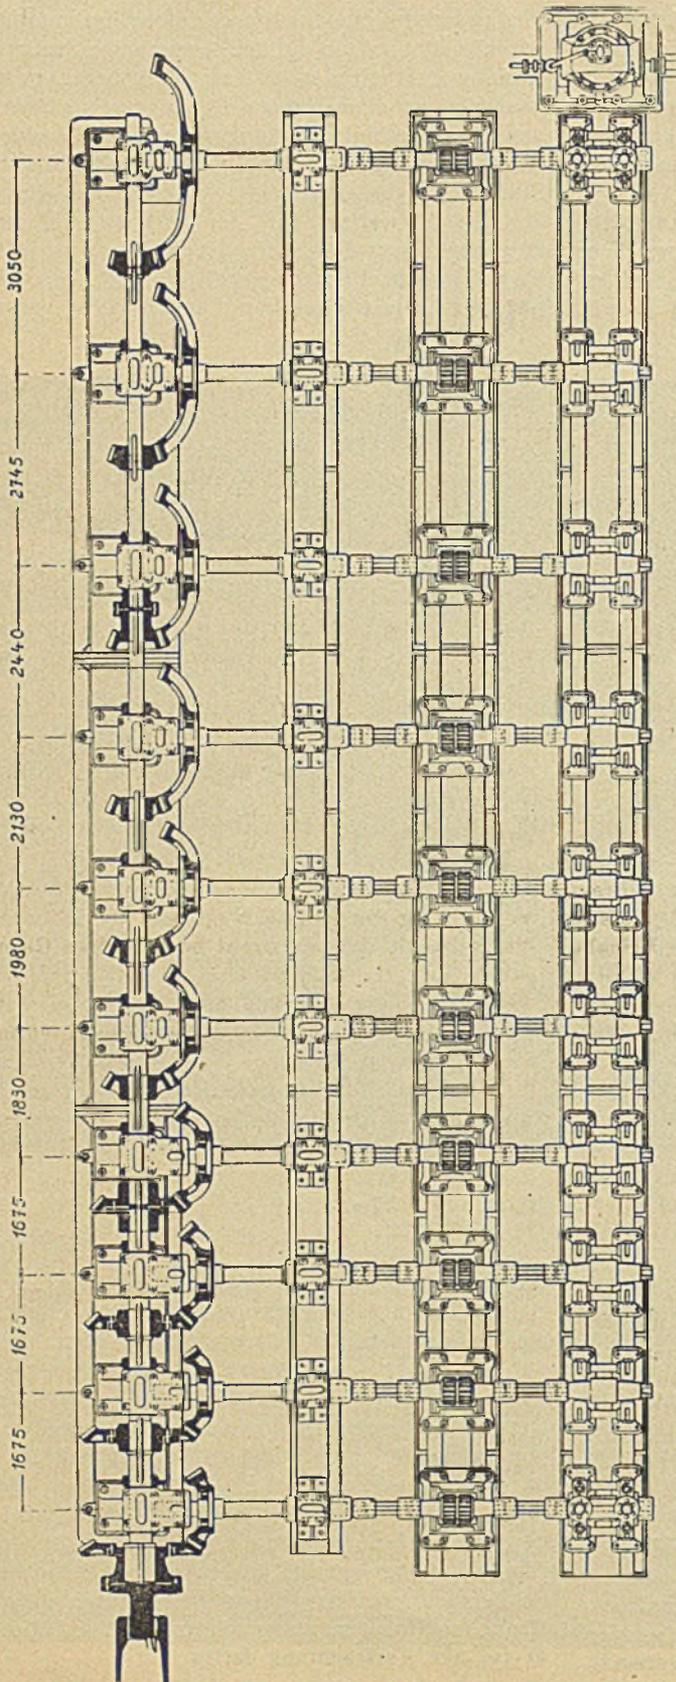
Plan des kontinuierlichen Walzwerks.
